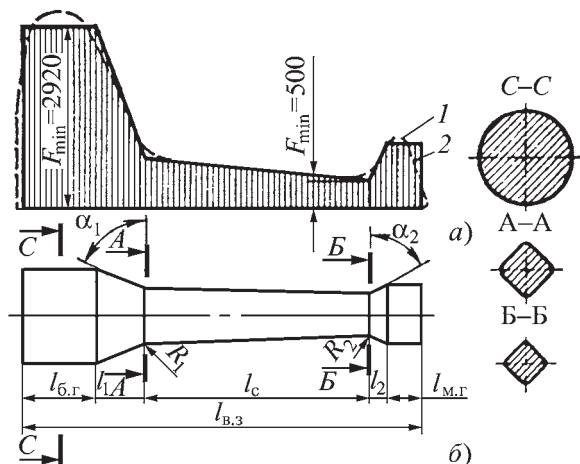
Построение вальцованной заготовки для поковки рычага:
